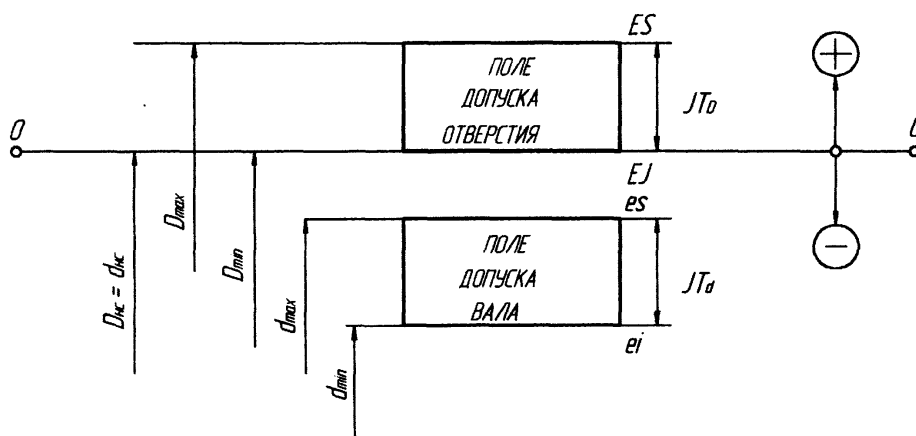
Схема полей допусков втулки и вала в соединении с зазором
